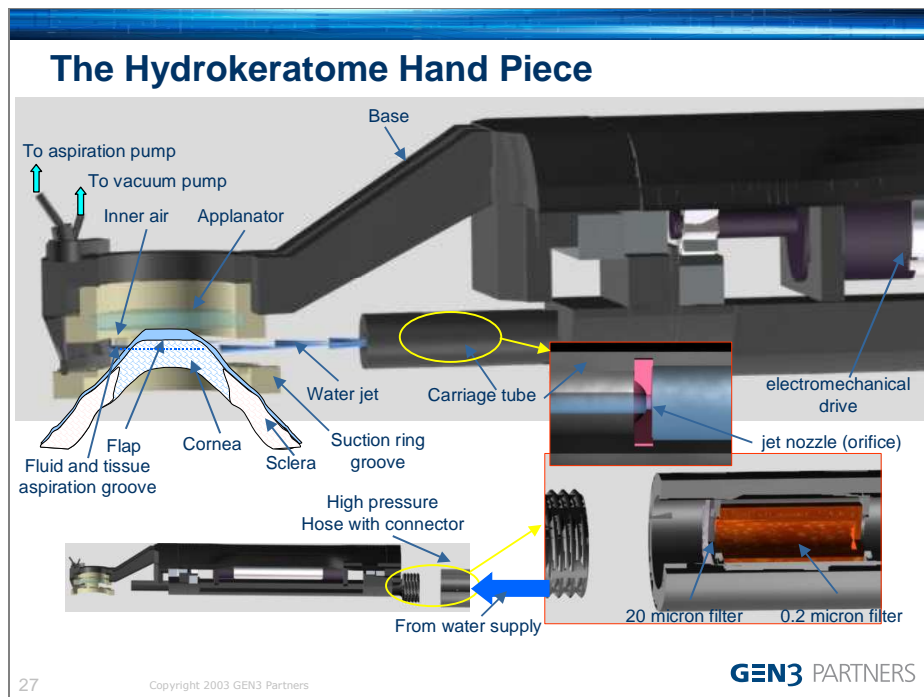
Внешний вид и устройство hand pieceе Гидрокератома
